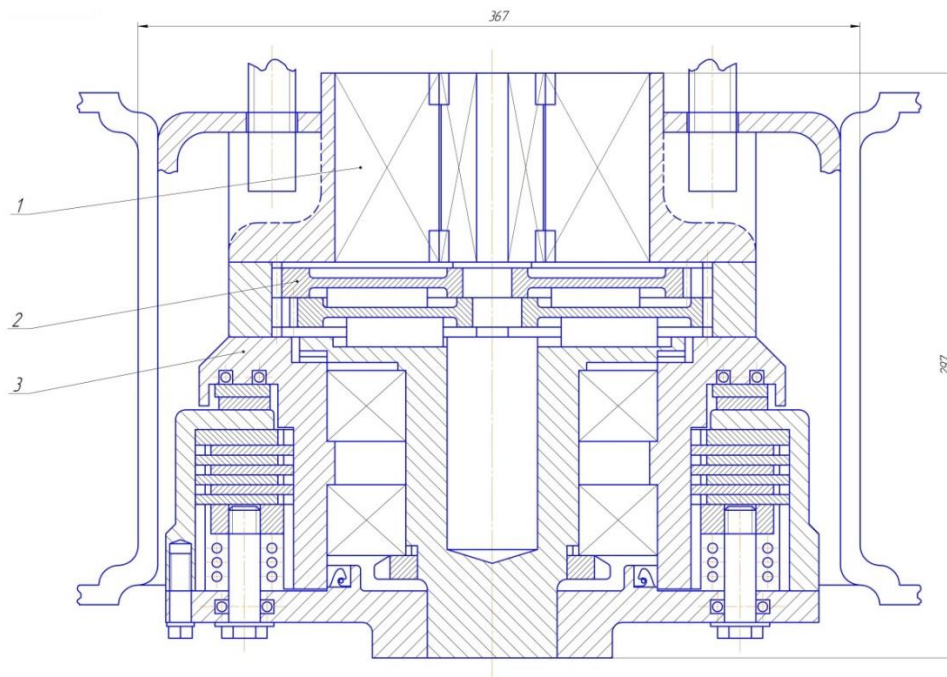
Разработанный волновой вариатор, установленный в мотор-колесо:
